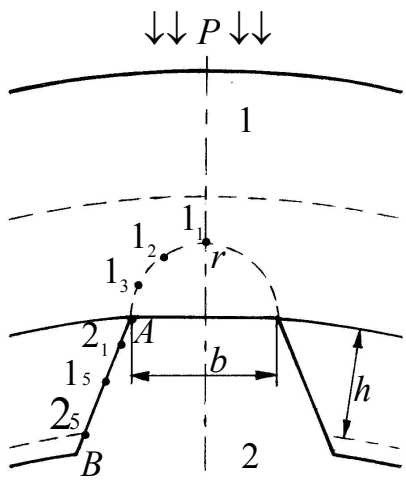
Схема формування внутрішніх шліців в трубній заготовці
